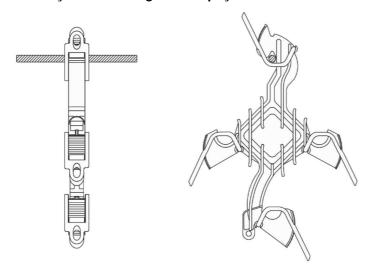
Amarrações e ancoragens – Espaçadores – Com travas integradas
